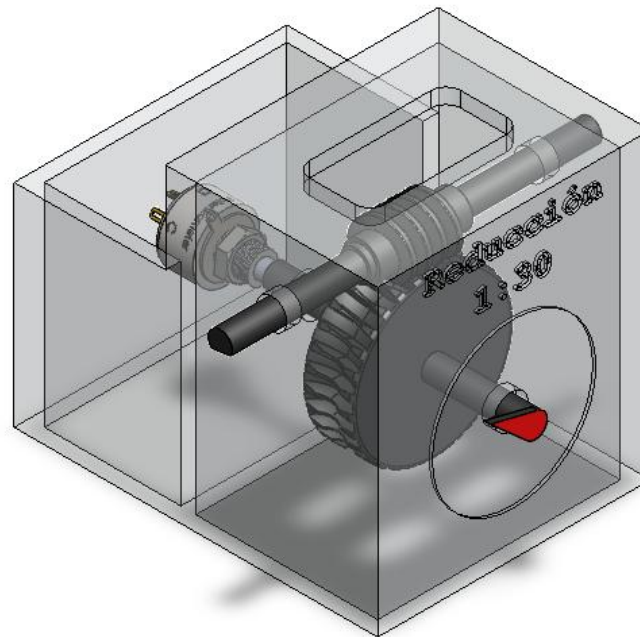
Modelo 3D del conjunto tornillo sinfín-corona en SolidWorks.
